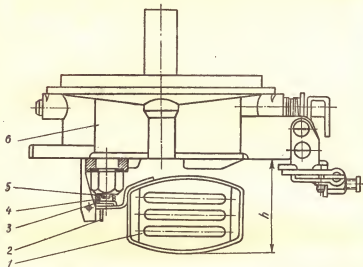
Проверка правильности положения поплавка карбюратора К-126Н: 1 — поплавок; 2 — ограничитель хода поплавка; 3 — язычок рычага поплавка; 4 — демпфирующая пружина; 5 — игольчатый клапан; 6 — крышка поплавковой камеры.
